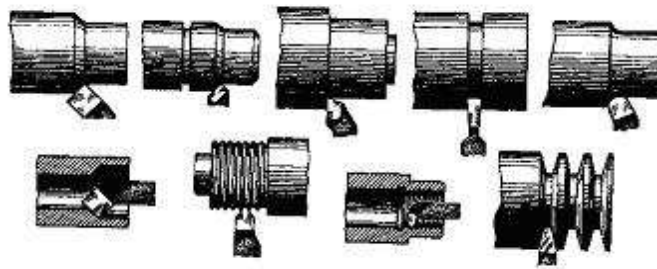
Способи обробки заготівель на токарських верстатах
